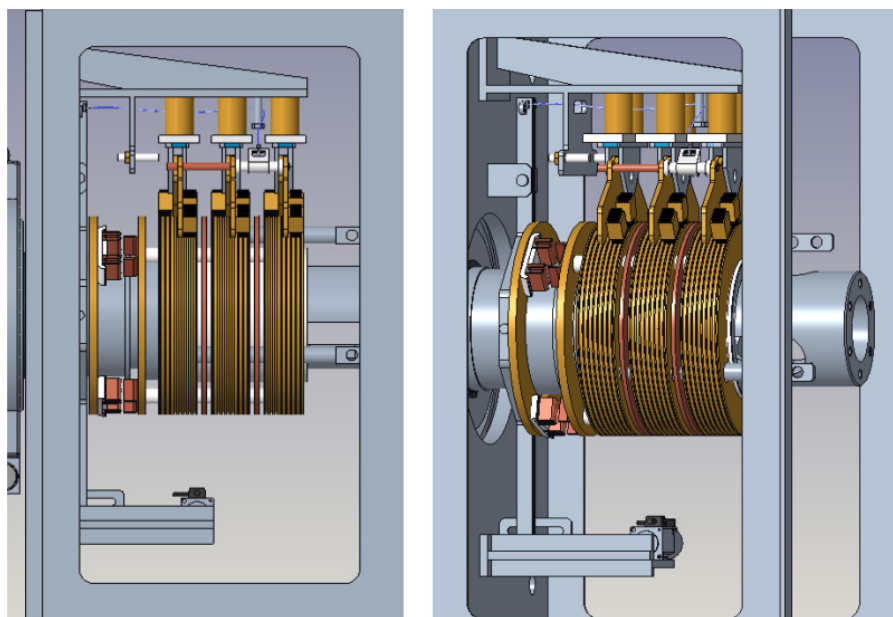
ЩКУ с приспособлением для подъема щеток и замыкания колец
